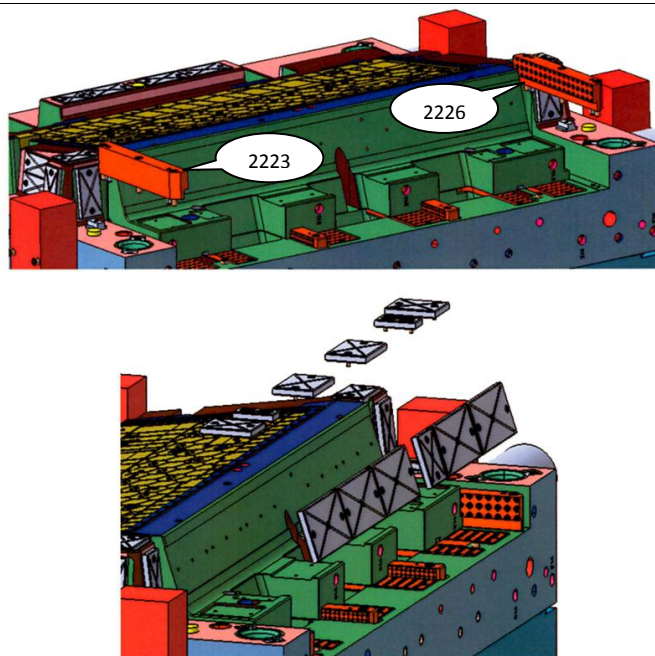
Sequência de montagem do movimento mecânico SI02.
